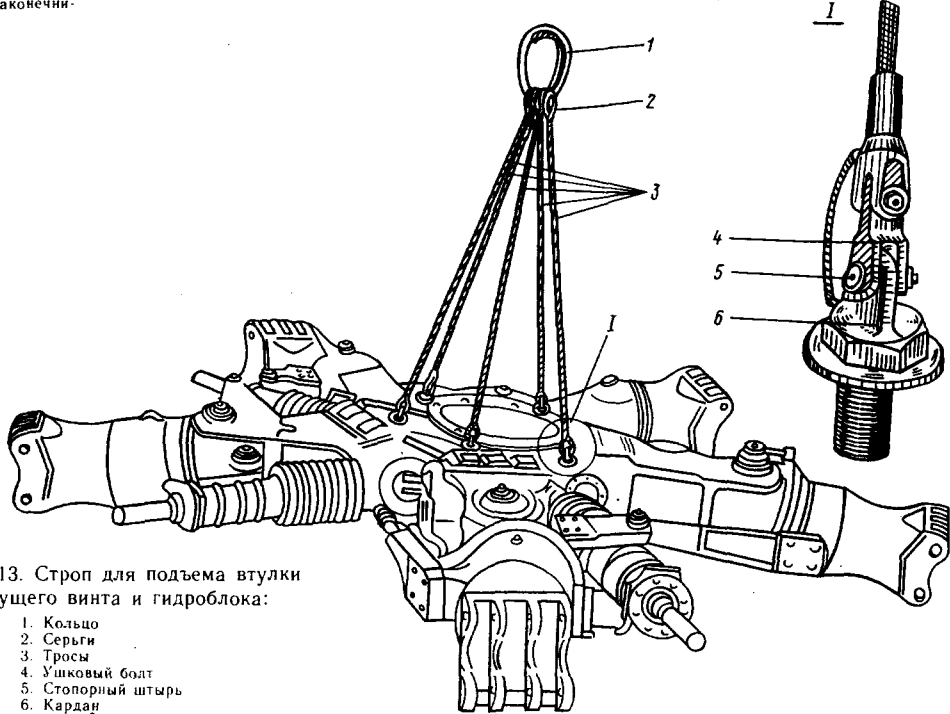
Строп для подъема втулки несущего винта и гидроблока:
